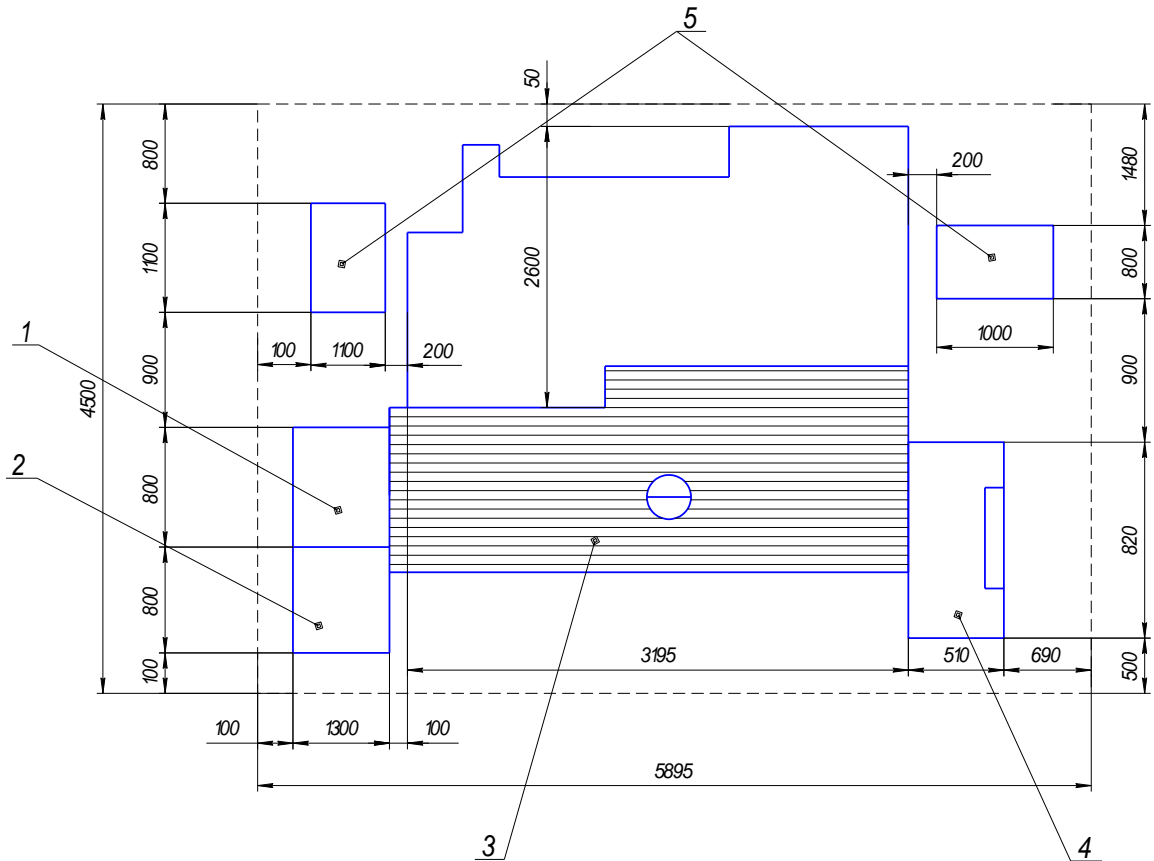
План робочого оператора верстата з ЧПК:
